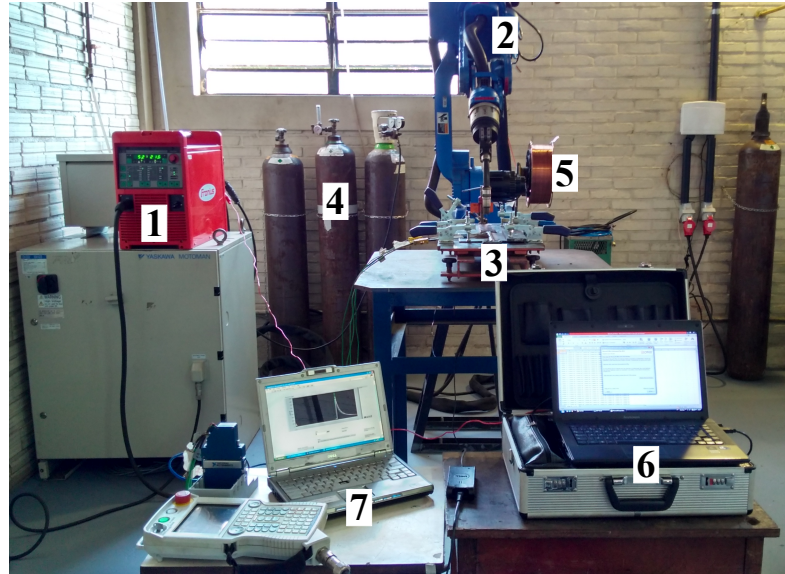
Equipamentos utilizados no processo de soldagem e aquisição de dados: (1) Fonte de soldagem; (2) Robô; (3) Sistema para fixação da peça; (4) Gás de Proteção; (5) Arame/Eletrodo; (6) Sistema de aquisição de tensão e corrente; (7) Sistema de aquisição de temperatura.
